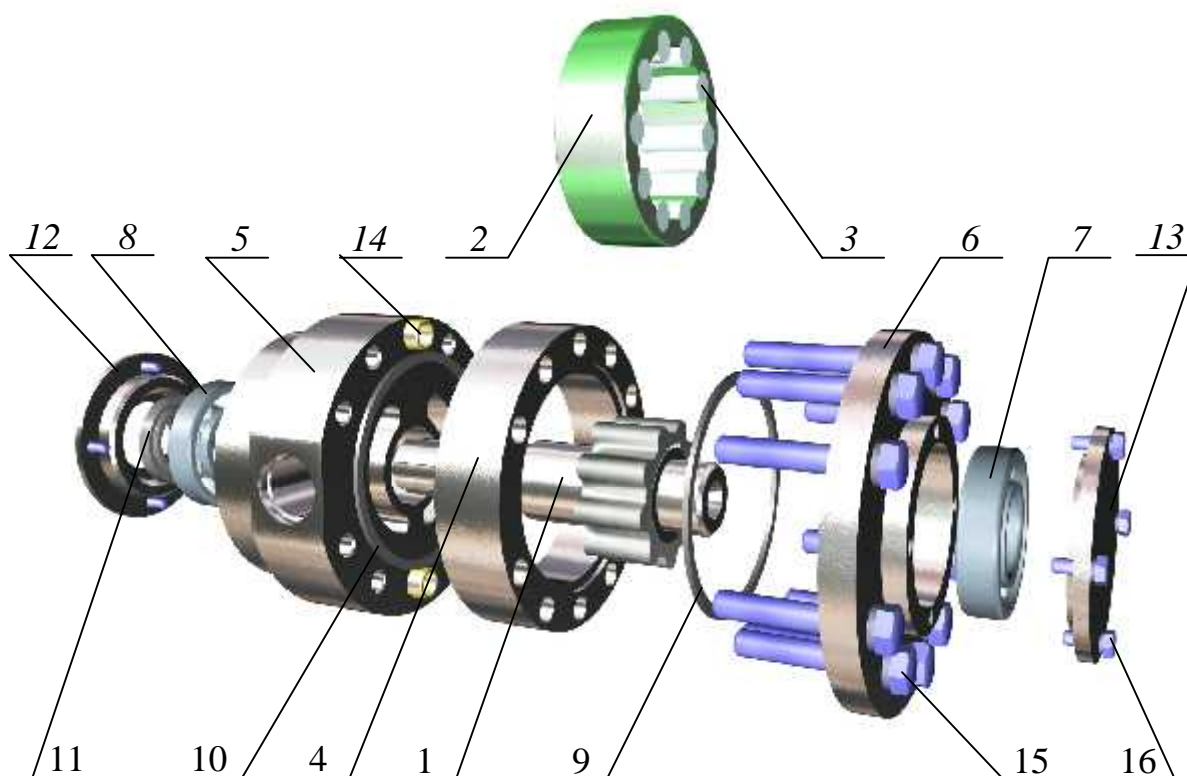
Героторная гидромашина: 1 – вал-шестерня; 2 – ротор; 3 – ролики (зубья); 4 – корпус; 5 – передняя крышка; 6 – задняя крышка; 7, 8 – подшипники качения; 9, 10 – кольцевые уплотнения; 11 – уплотнение вала; 12 – крышка уплотнения; 13 – крышка подшипника; 14 – направляющие; 15, 16 – соединительные болты.
